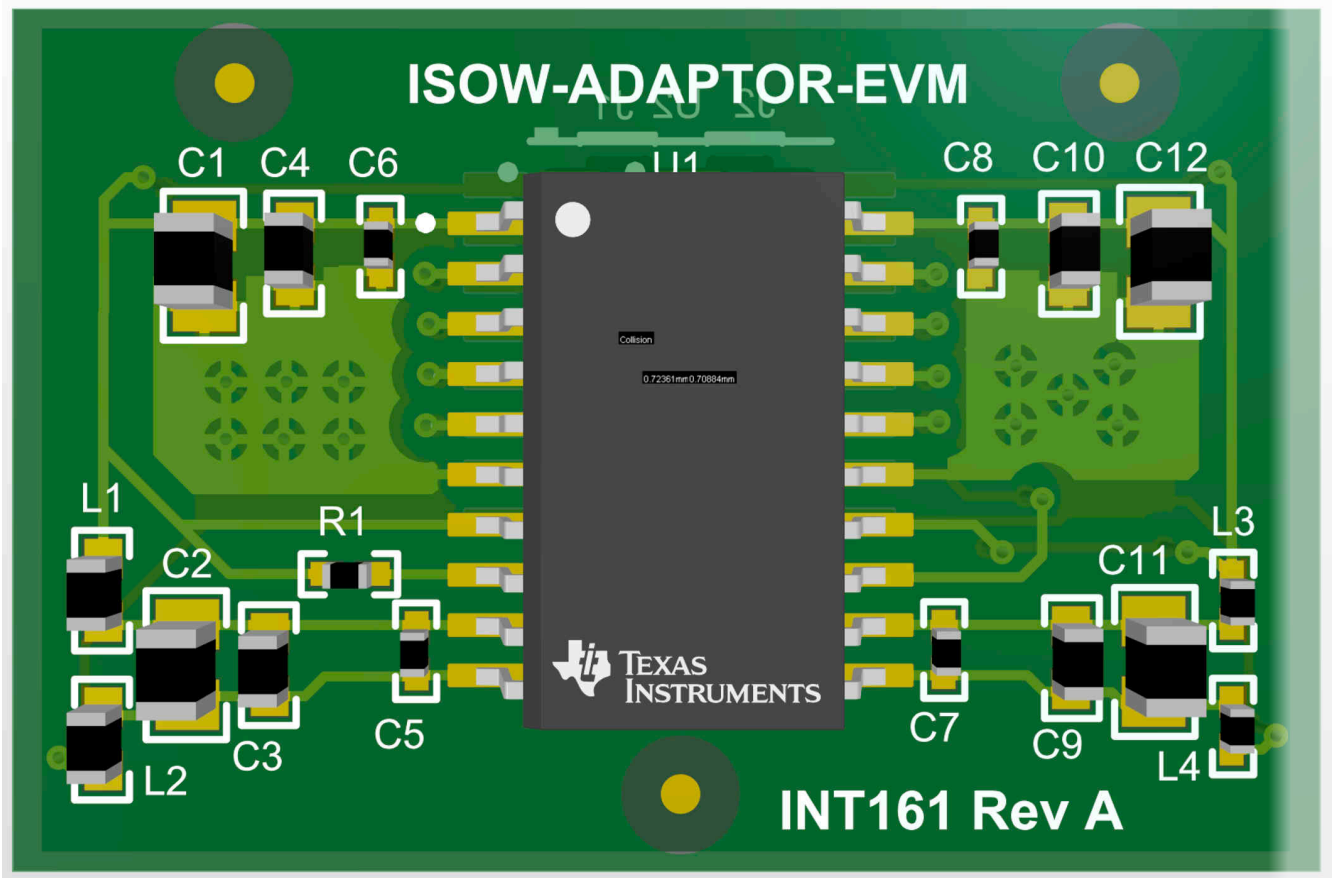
ISOW-ADAPTOR-EVM PCB 3D 图
